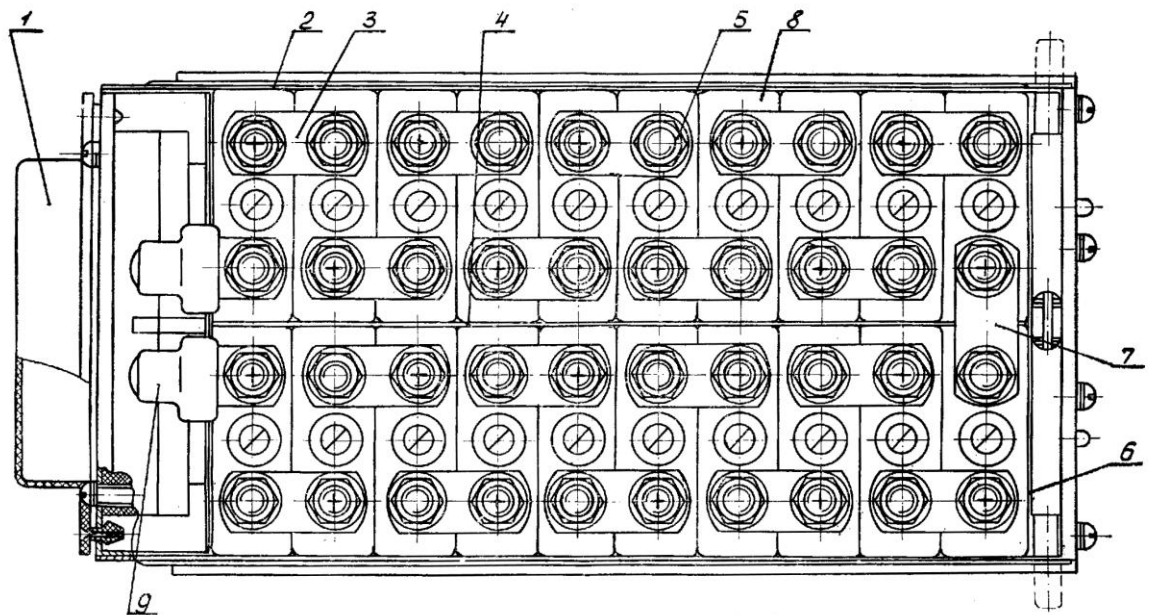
Вид на акумуляторну батарею 20ЕКБН-25 зверху. 1 - розетка штепсельного роз'єму; 2 - корпус; 3 - сполучна шина (накладка); 4 - прокладка; 5 - гайка; 6 - прокладка задня; 7 - шина; 8 - акумулятор (елемент) НКБН-25; 9 - висновок. Для під'єднання батареї до бортової мережі на задній стінці корпусу розташований штепсельний роз'єм РША-1.
